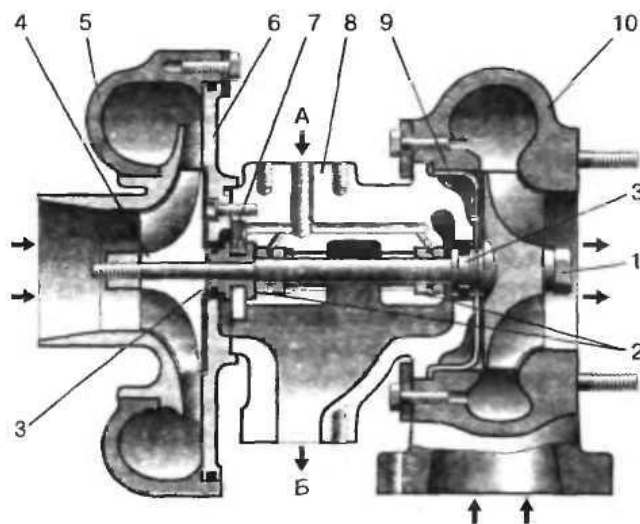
Візуалізація конструктивних особливостей сучасного турбокомпресора: 1 - ротор з колесом турбіни; 2 - підшипник ротора; 3 - ущільнення ротора; 4 - колесо компресора; 5 - корпус компресора; 6 - корпус ущільнення компресора; 7 - гідродинамічний під'ятник; 8 - корпус підшипників; 9 - кожух ущільнення; 10 - корпус турбіни; А - вхід мастила; Б - злив масла
